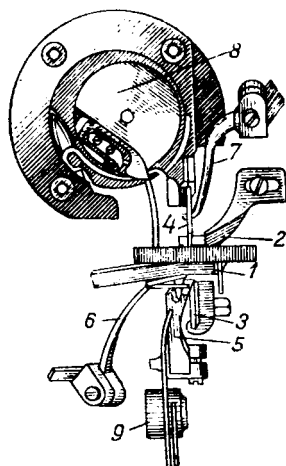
Схема рабочих органов машины для пристрочки подошвы
